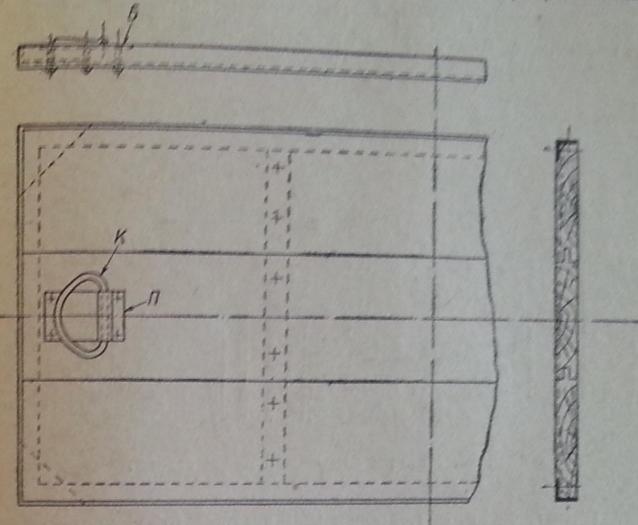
Крышка люка: К — кольцо люка, П — металлическая планка для крепления кольца и крышки люка, Б — болты, крепящие планку.
